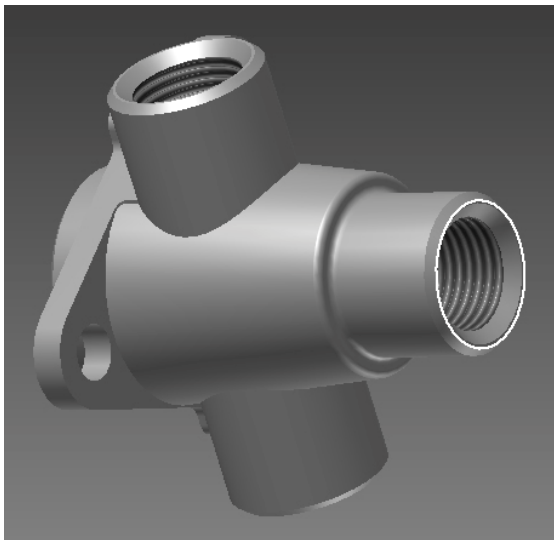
Примеры моделей корпусных деталей для выполнения сборочных чертежей
